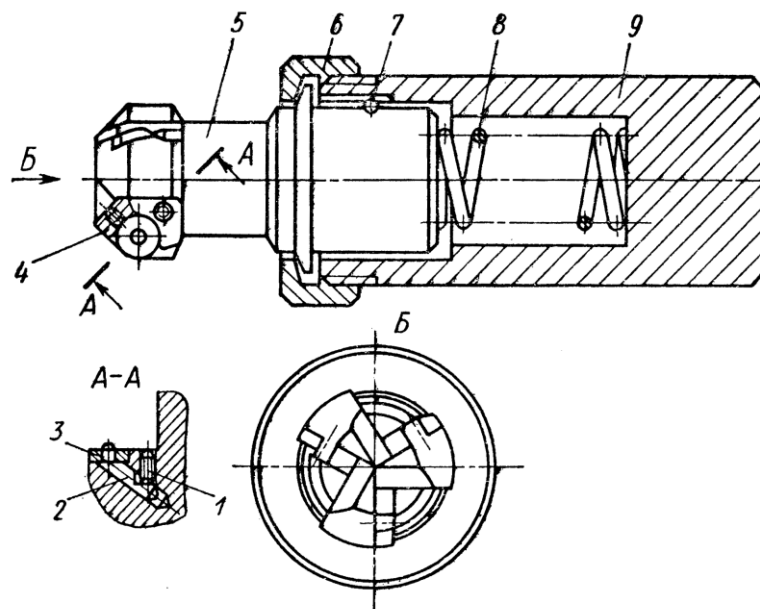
Трилезова коливна самовстановлювальна розвертка
